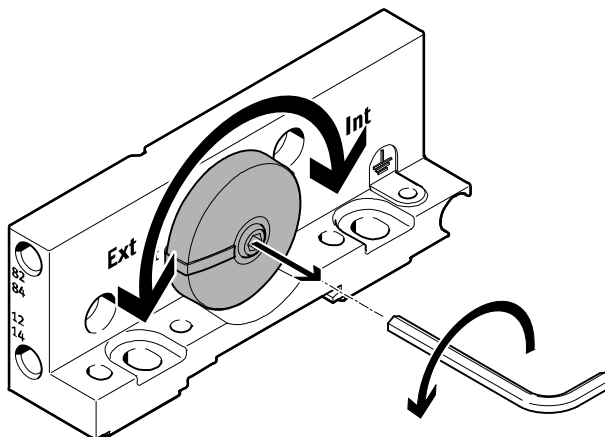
Umbau bei rechter Endplatte ohne Versorgungsanschlüsse
